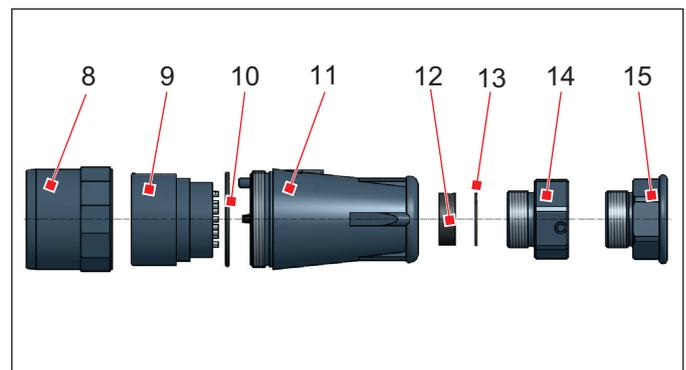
Ersatzteile für UIC 558 Kabelstecker
